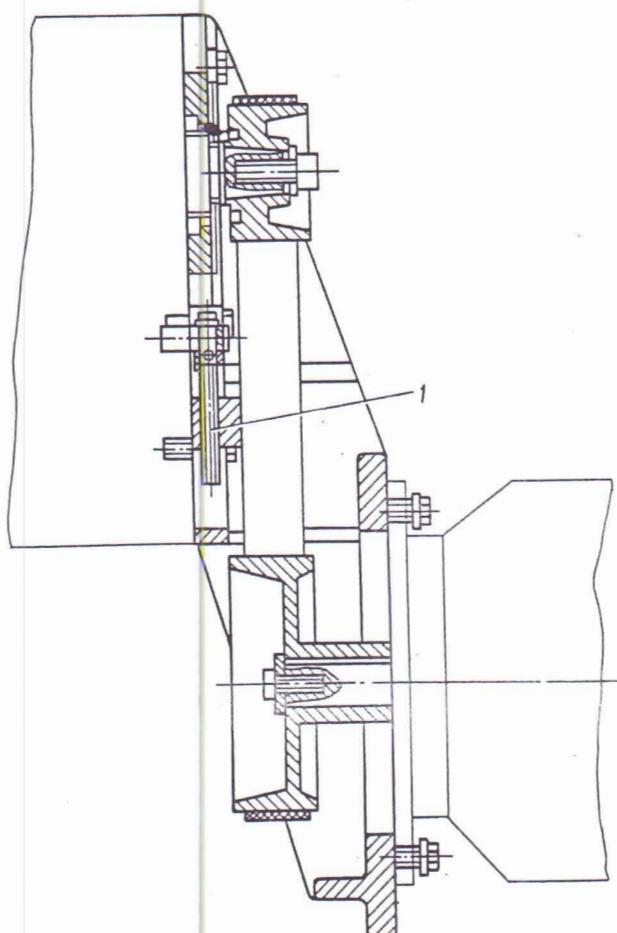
Регулирование натяжения ремня главного привода шлифовального круга
